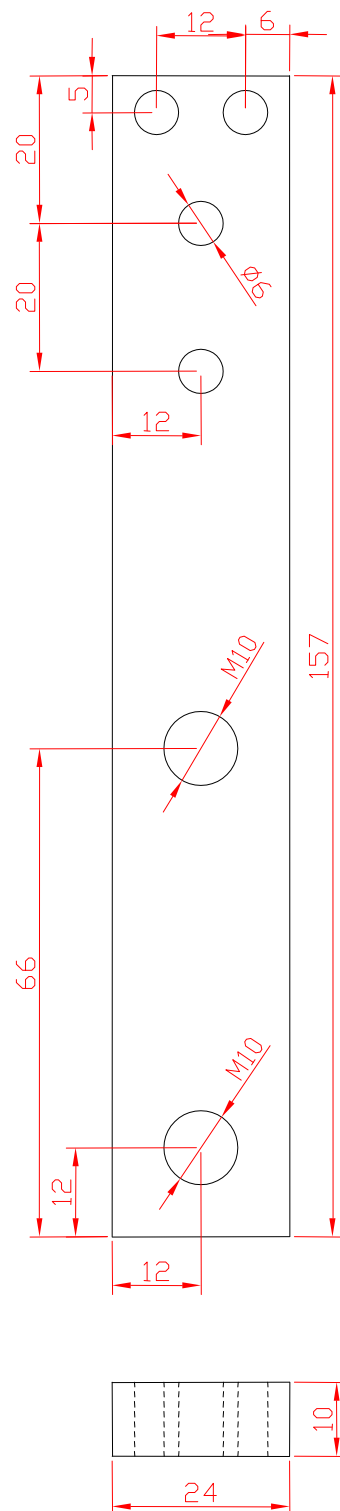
Vista en planta y frontal de la base de los soportes verticales.
